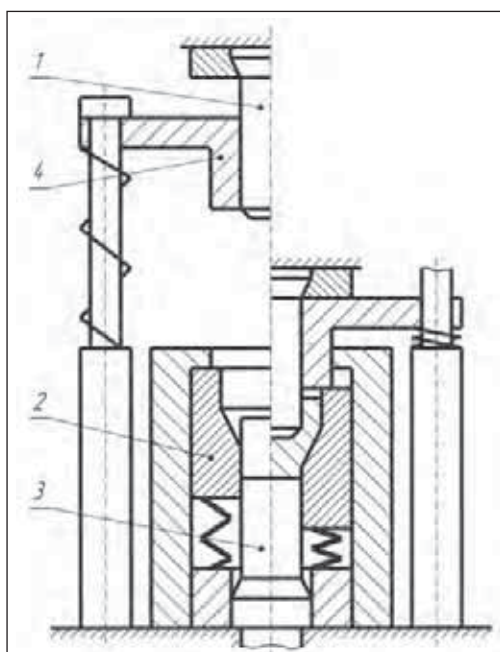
Штамп для закрытой прошивки, совмещенной с раздачей заготовки, в движущейся матрице
